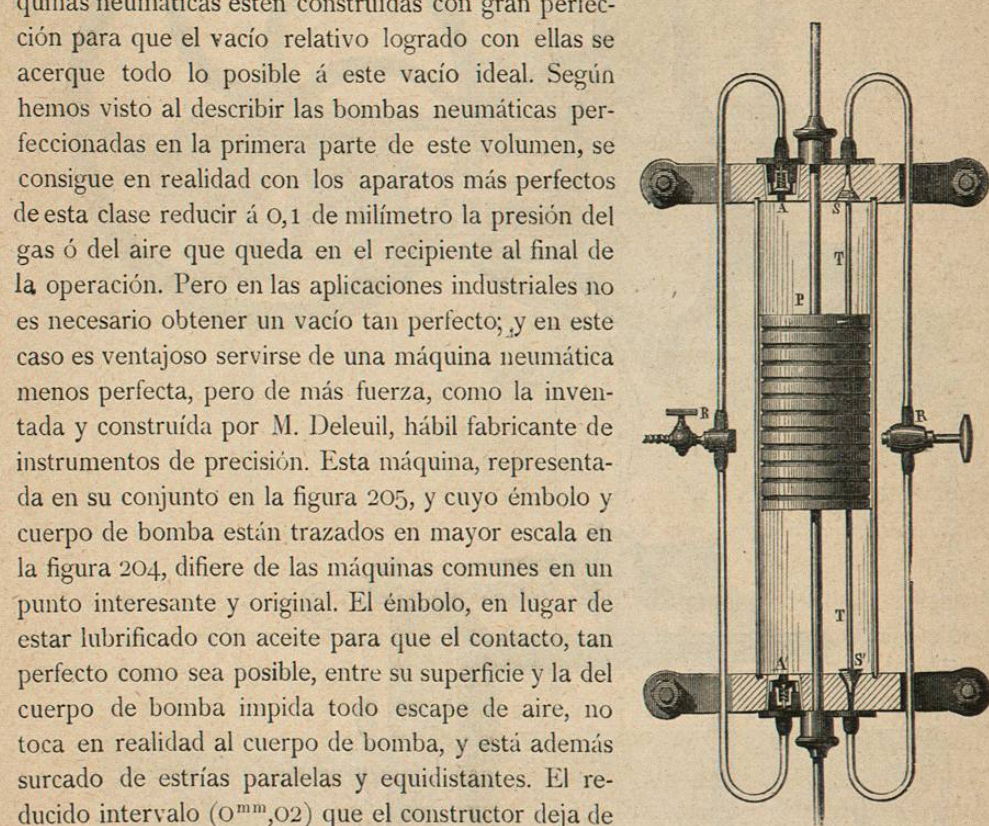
Émbolo de la máquina neumática de Deleuil
